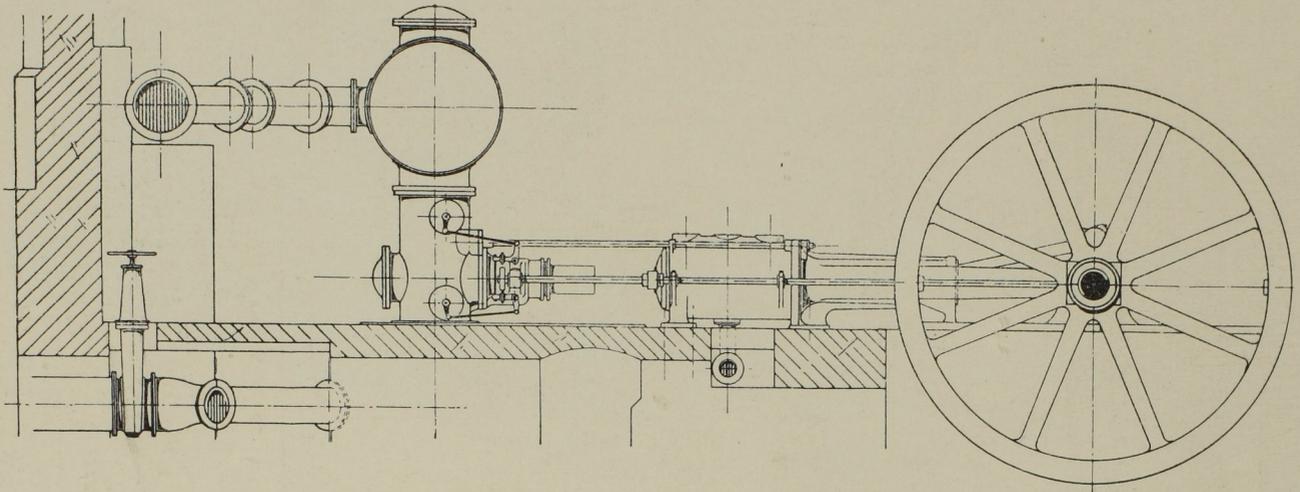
Seitenansicht der Pumpmaschine und Rohrleitung. Massst. 1:90.
